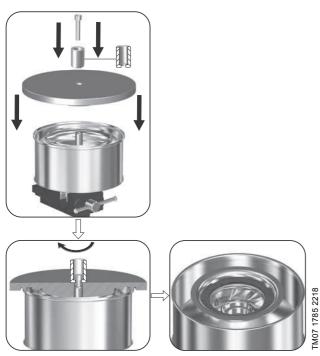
Уплотнительное кольцо, стопор уплотнительного кольца и камера, установленные в приспособлении L.
